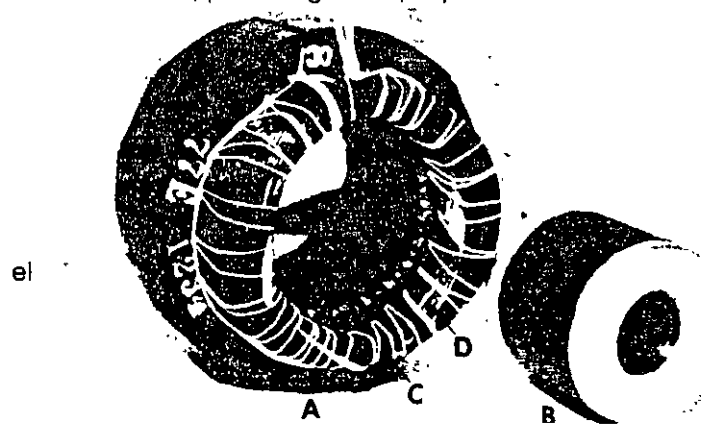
Estator y rotor de un motor hermético de 1/4 hp de fase partida: A, estator; B, rotor; C, devanado de marcha; D, devanado de arranque (Cortesía de General Electric Company, Hermetic Motor Department)
